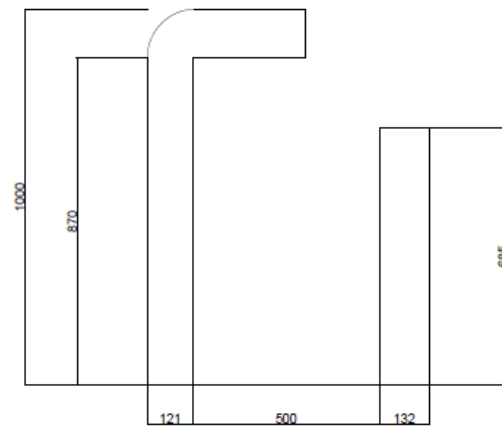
Planta com as dimensões do acessório proposto, medidas em mm.
